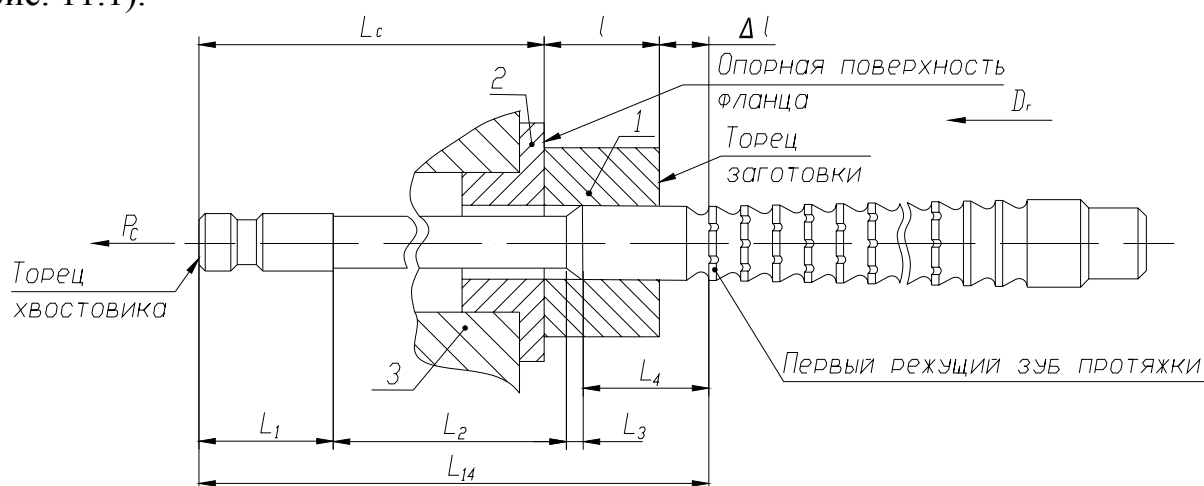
1. Положение протяжки на станке перед началом протягивания: 1 – заготовка (обрабатываемая деталь); 2 – опорный фланец; 3 – опорная планшайба станка; P_c – тяговая сила протяжного станка
